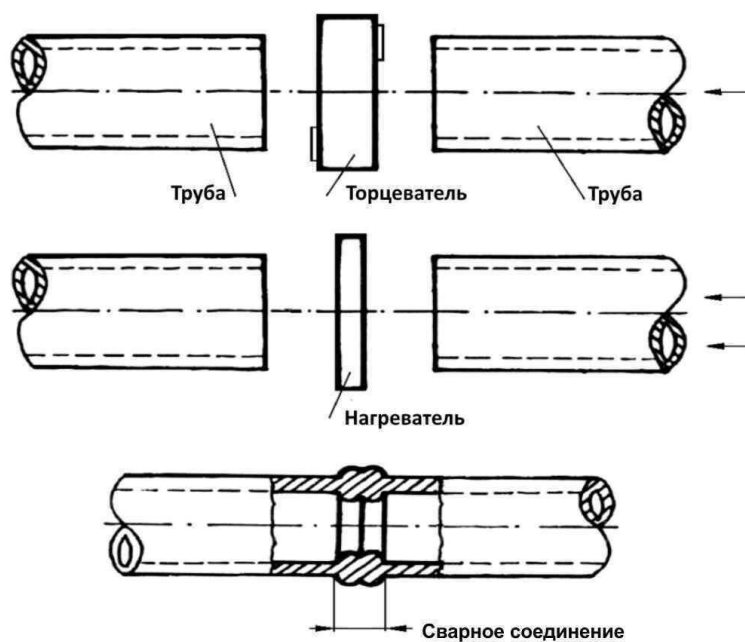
Контактная сварка пластмассовых труб
